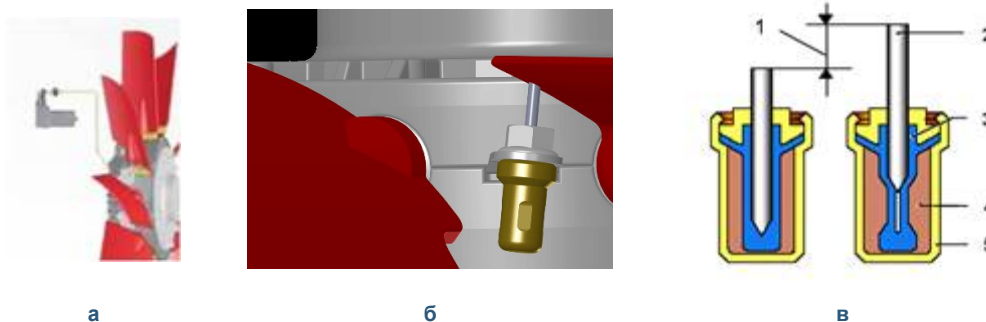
Регулювання лопатей вентилятора Cleanfix:
